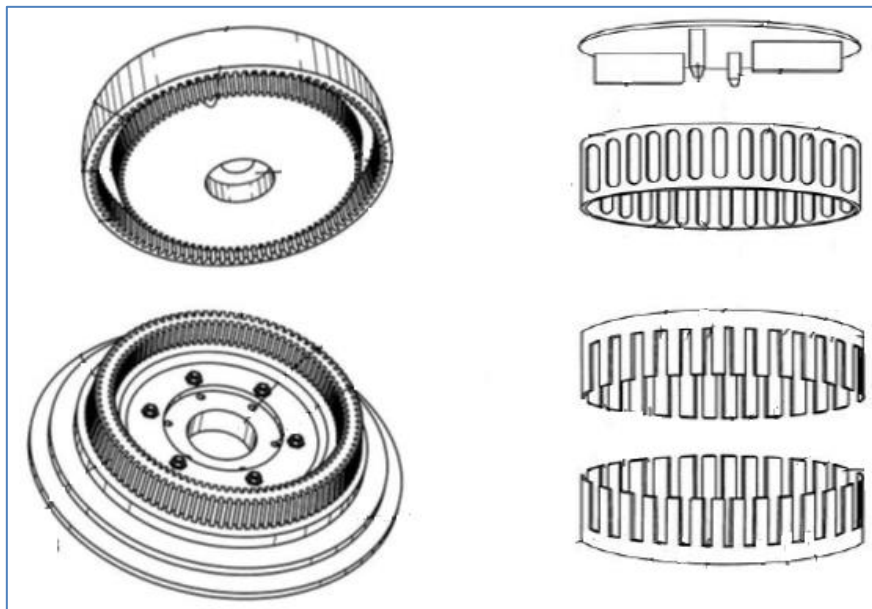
Despiece y perspectiva de modelos de conjunto rotor-estator. Fuente: [12]
